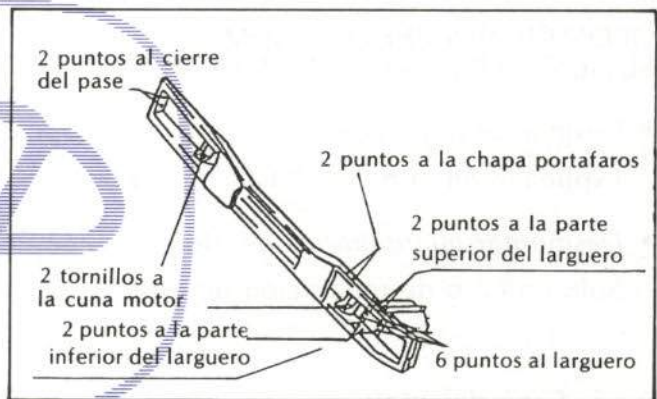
Unión de la traviesa inferior a la carrocería.
